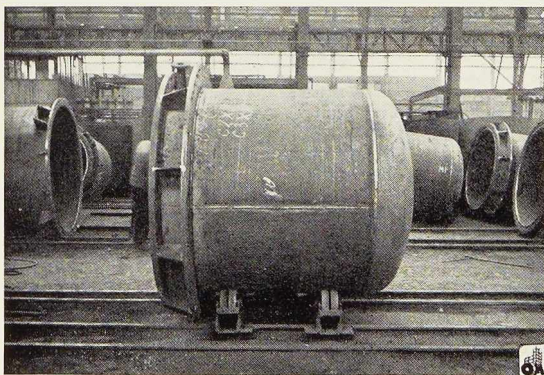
Cuve montée sur des galets pour l'exécution des soudures à l'intérieur.
